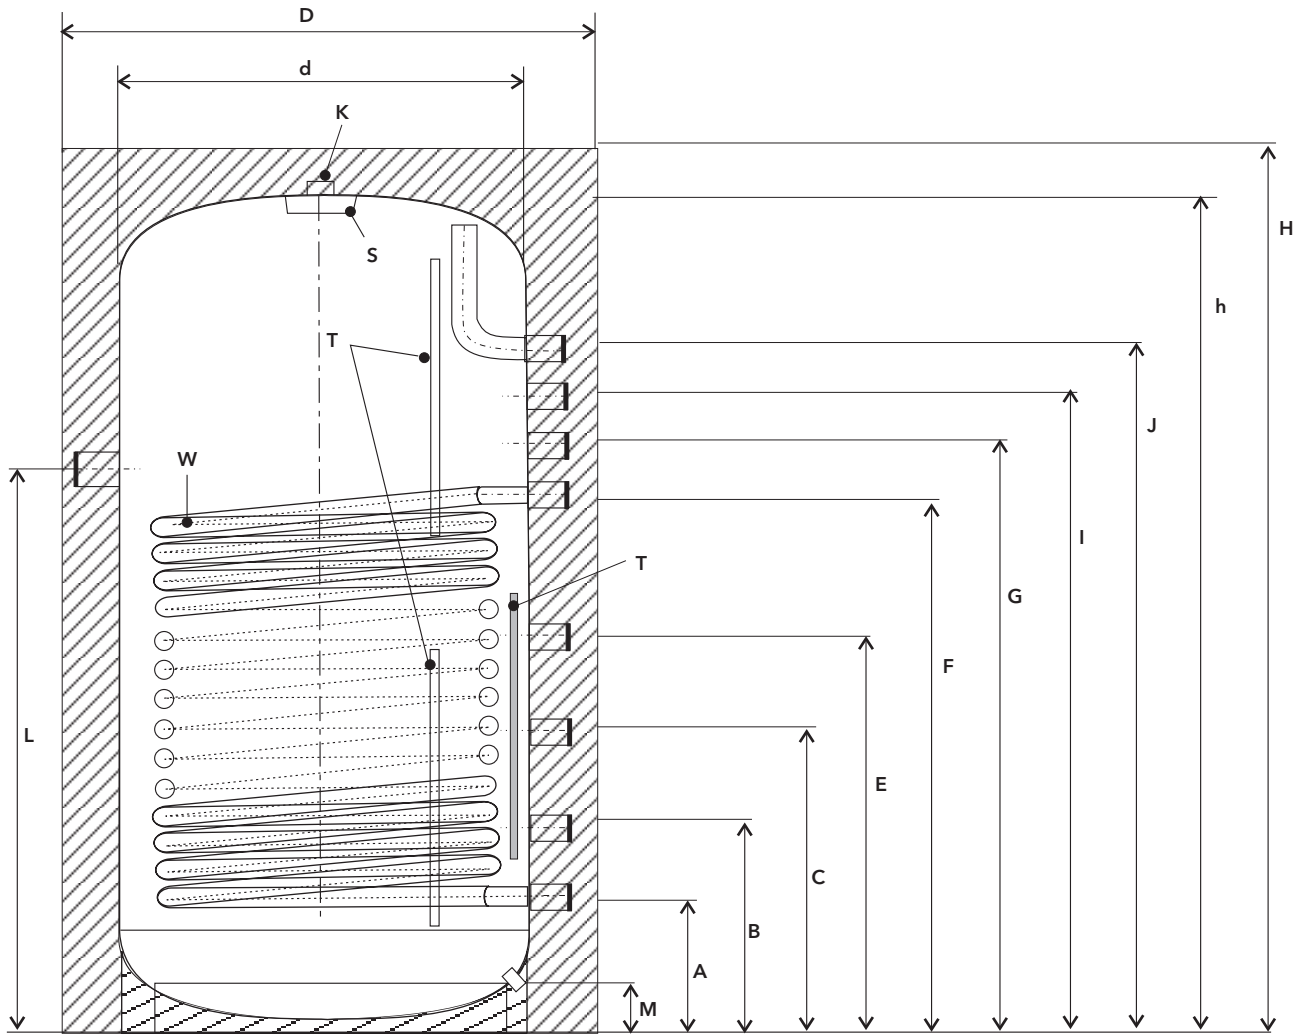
RATIO-HP Pufferspeicher im Schnitt mit Maßbezeichnung
